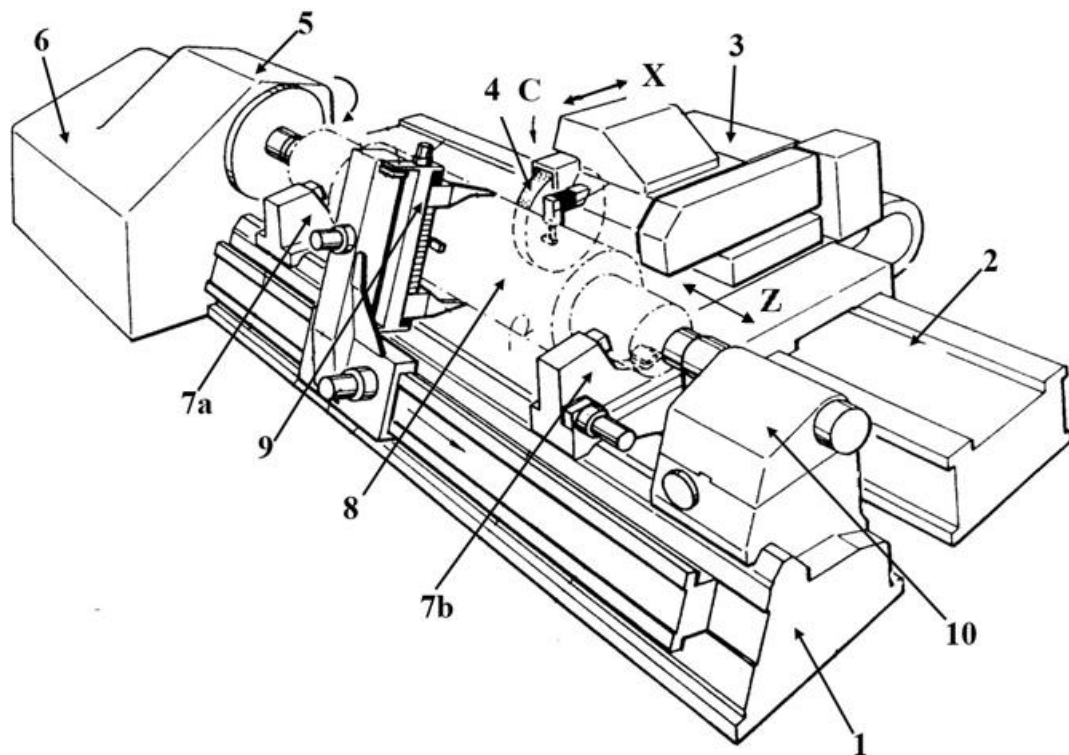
Equipements techniques de la rectifieuse 850 A.
